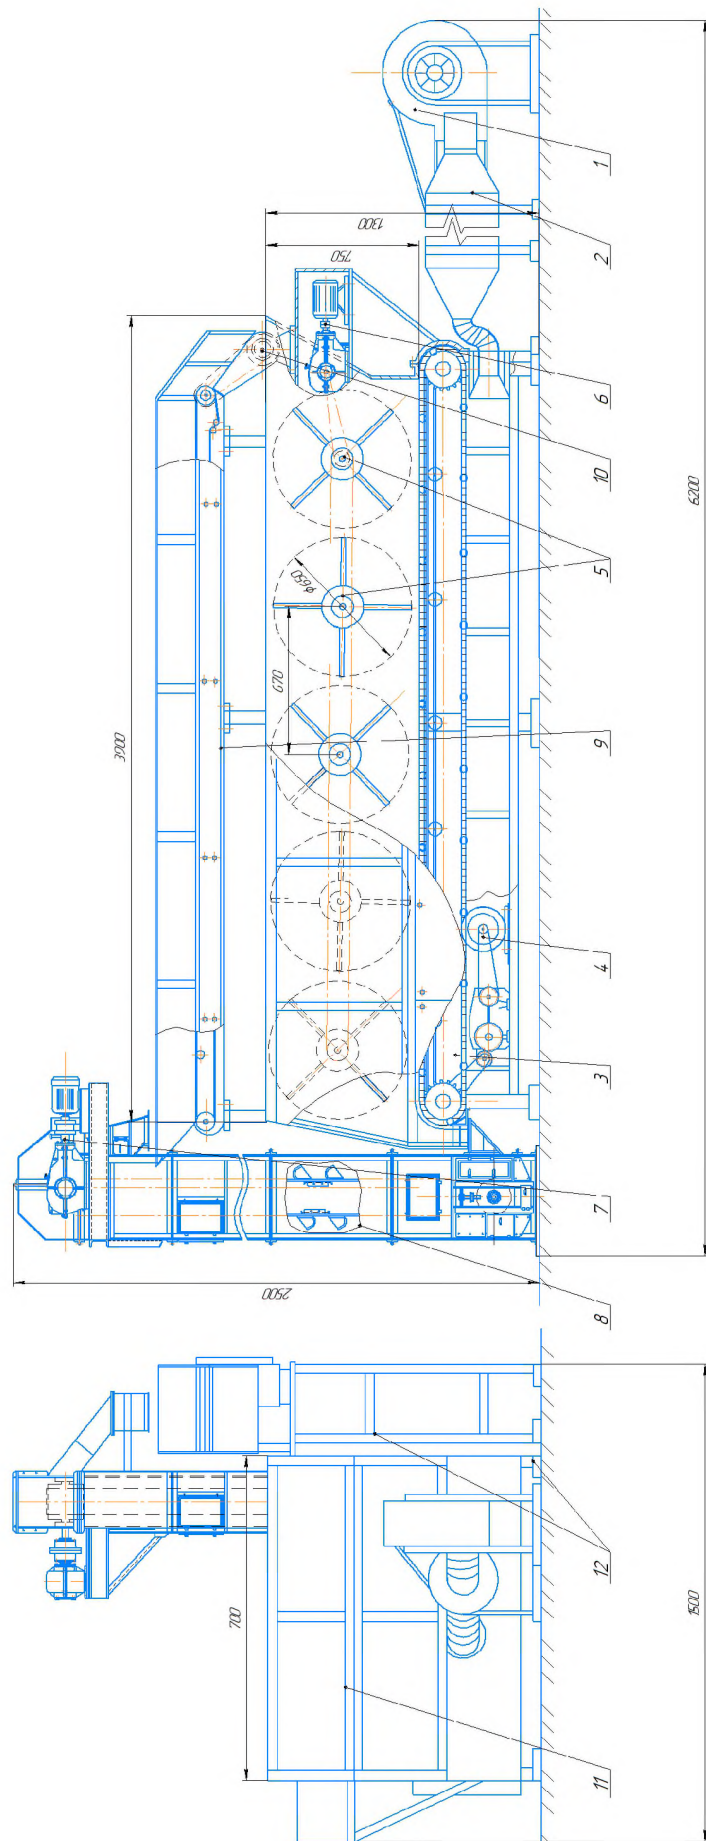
Принципова схема напівної сушарки. 1 – вентилятор; 2 – нагрівач повітря; 3 – транспортер; 4 – привод транспортера; 5 – ротор; 6 – привод; 7 – привод ковшового елеватора; 8 – ковшовий елеватор; 9 – вивантажувальний транспортер; 10 – привод вивантажувального транспортера; 11 – бункер; 12 – рама
